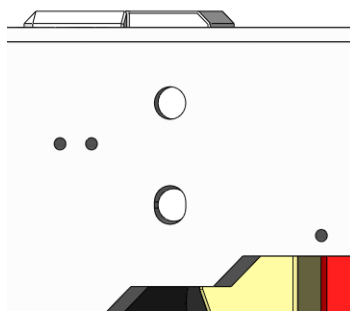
Крепление направляющих вдоль одной из координатных осей станка
